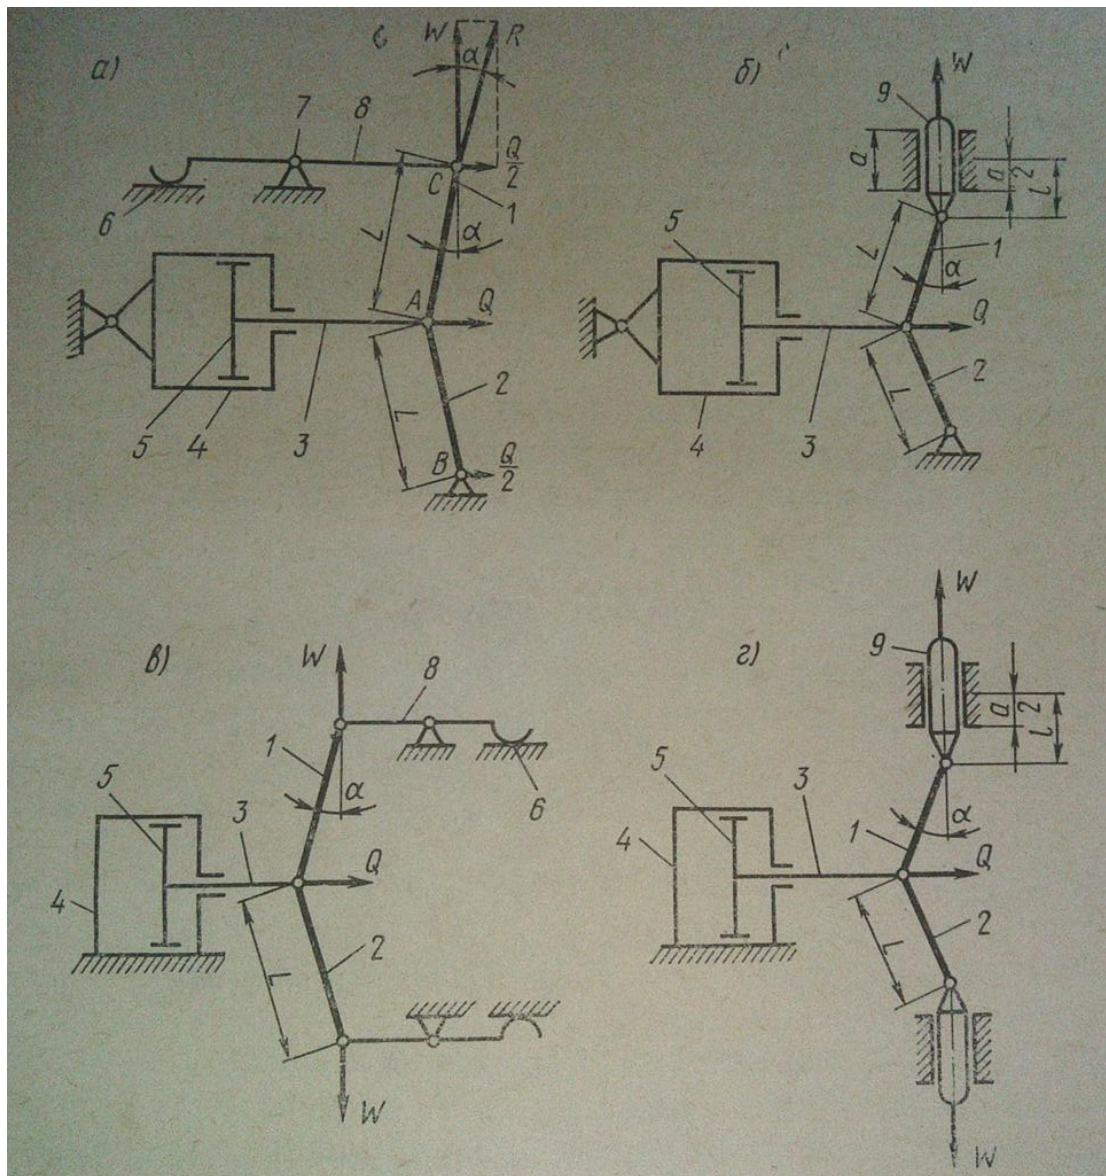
Схеми двохважельних шарнірних механізмів
